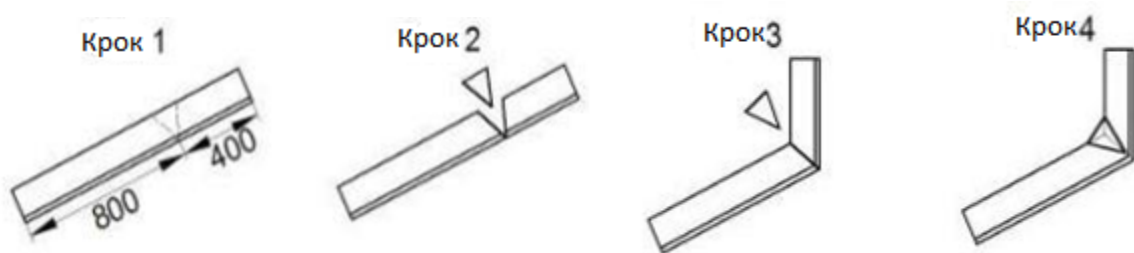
Схема виготовлення чобітка для установки зворотного склепіння кріплення КМП-А3
